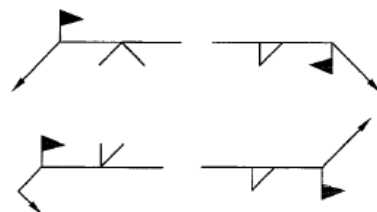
Símbolos de la Soldadura de Campo. [15]
